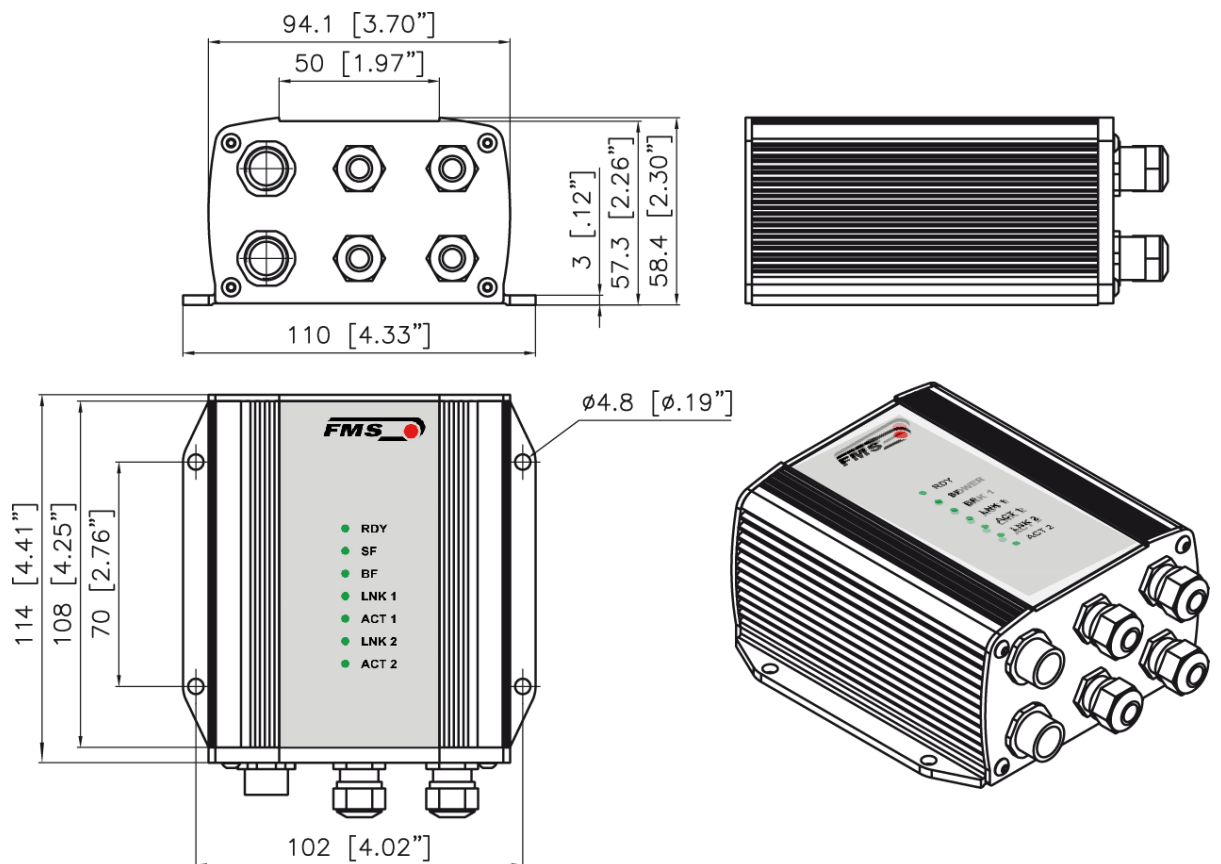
EMGZ492.W.PNET Gehäuse für Wandmontage
